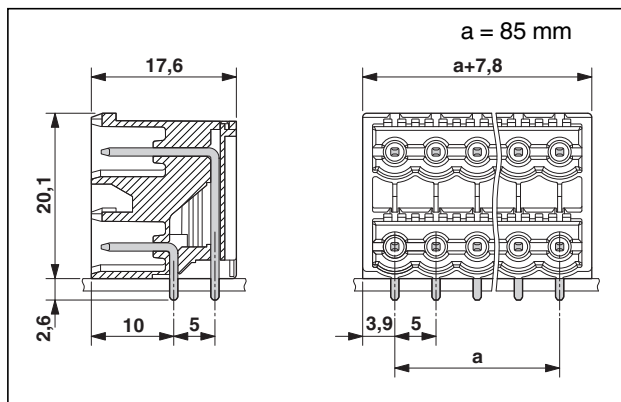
Abmessungen CCDN 2,5/18-G1 P26 THR
